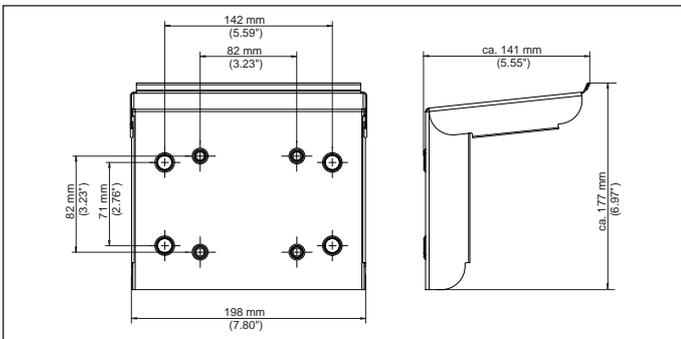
Dimensioni protezione dall'irradiazione solare VEGAMET 841, 842
